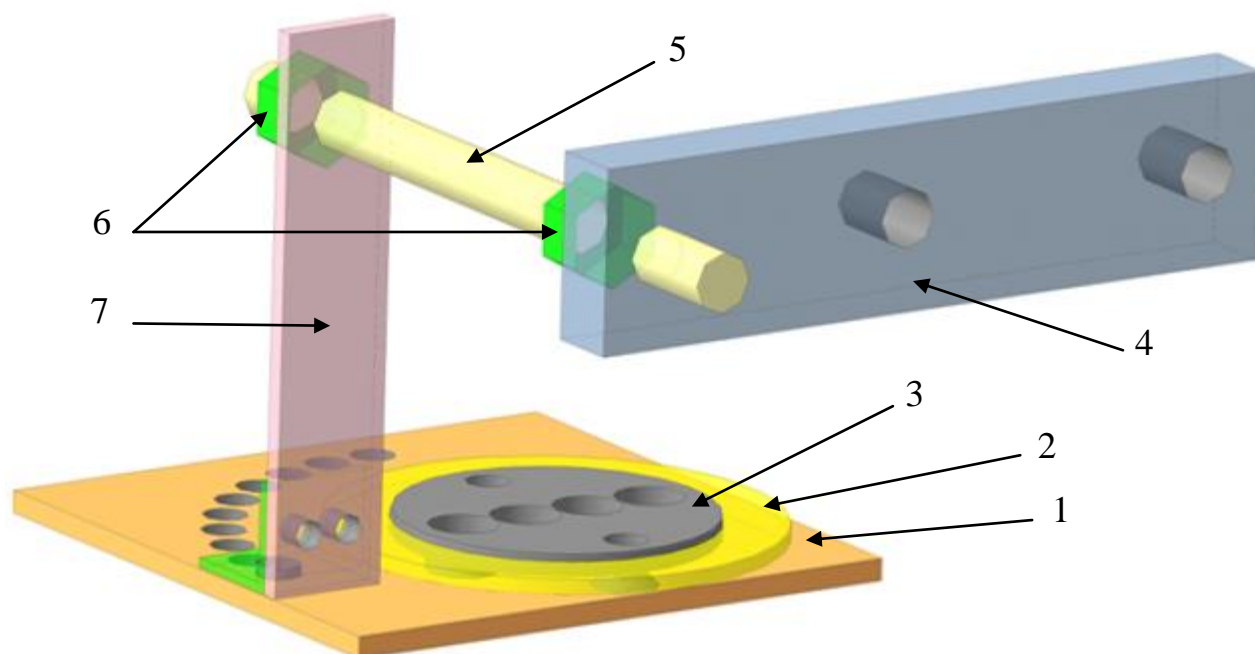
Схема поворота инструментальной оснастки на заданный угол α : 1 – поворотная пластина, 2 – гайка (условное изображение), 3 – сепаратор, 4 – планка, 5 – шпилька, 6 – контргайки, 7 – соединительная планка
